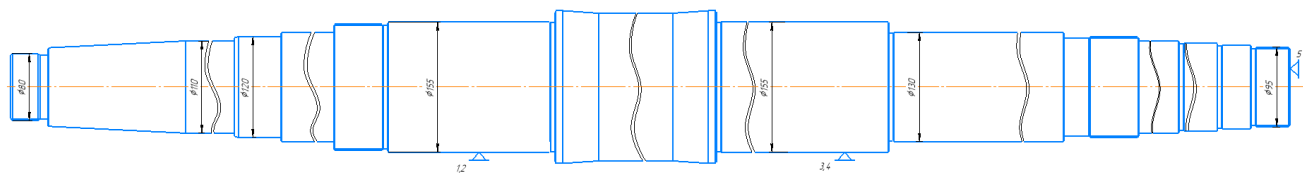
Схема базування деталі Вал Н12.178.34.01 у виробі.
